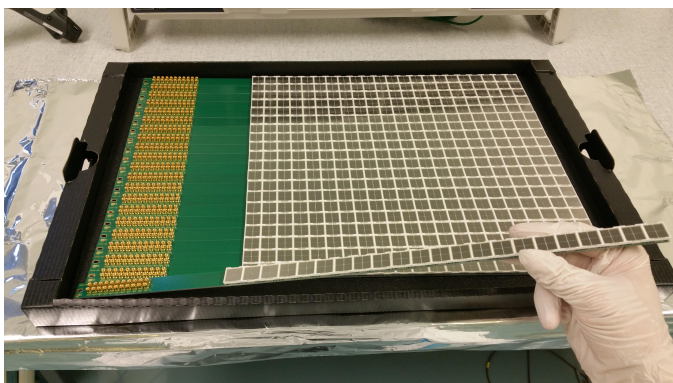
PCB に載せられた MPPC。1 つの PCB に 22 個の MPPC を載せることができる。
